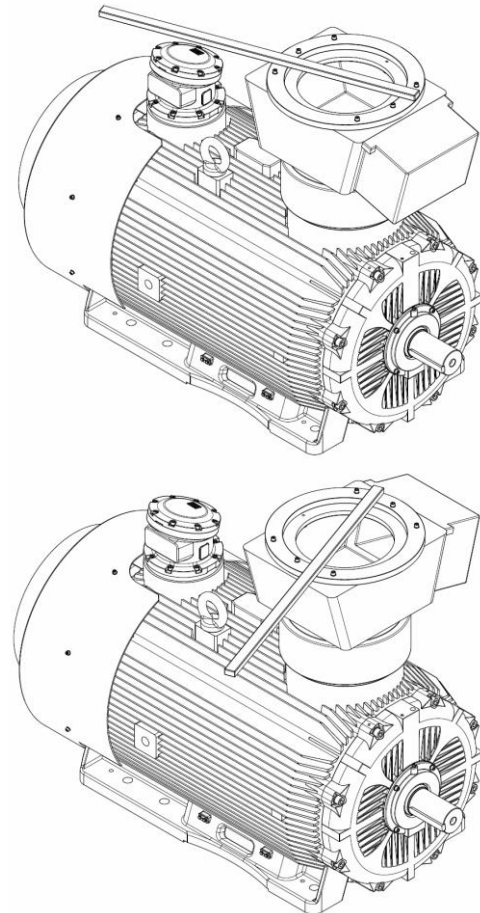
Поворот СКК с помощью поворотного приспособления
